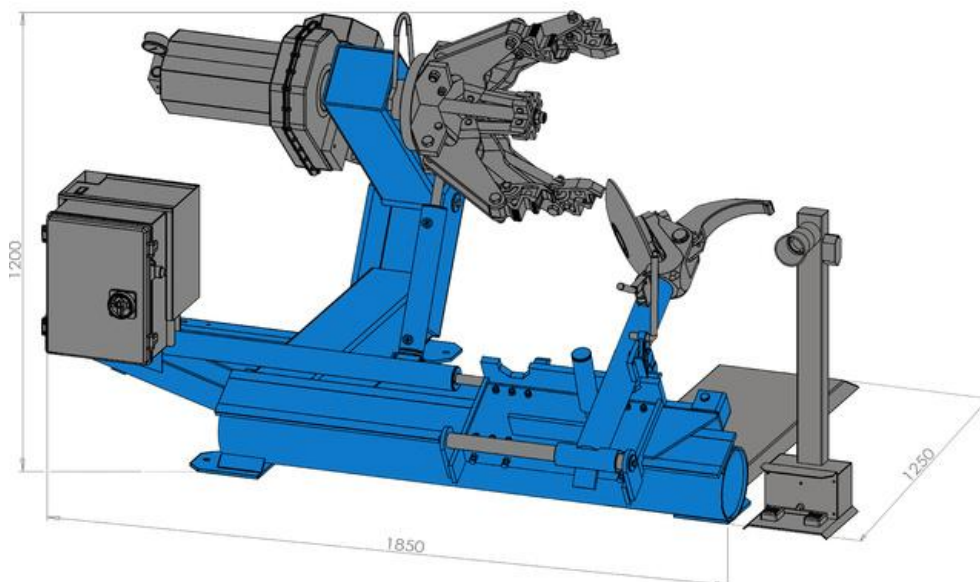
Шиномонтажный стенд КТ-С-280/Е
